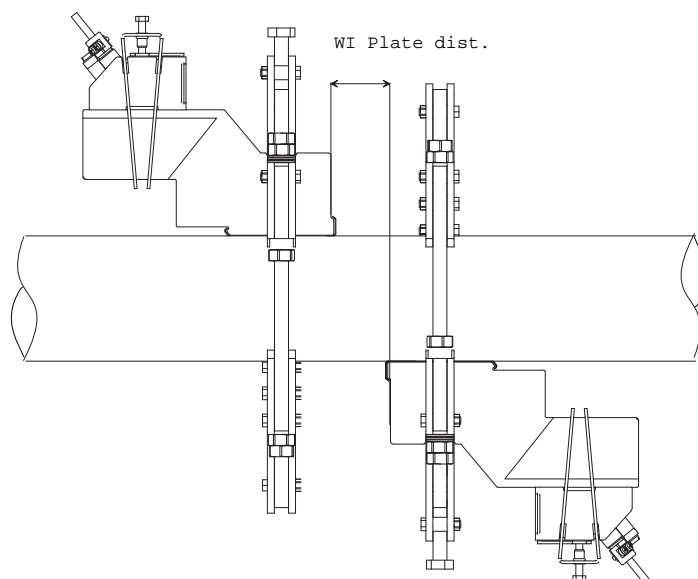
Установка второй стыковочной пластины в креплении к трубе (установка с резьбовыми шпильками)
